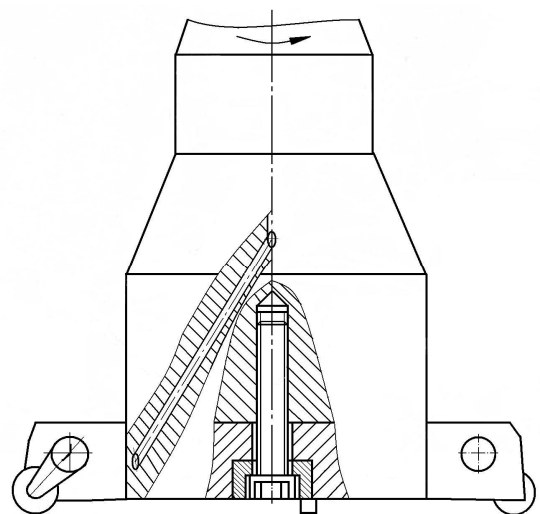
Торцева фреза касетного типу з круглими пластинами з ПКНБ
